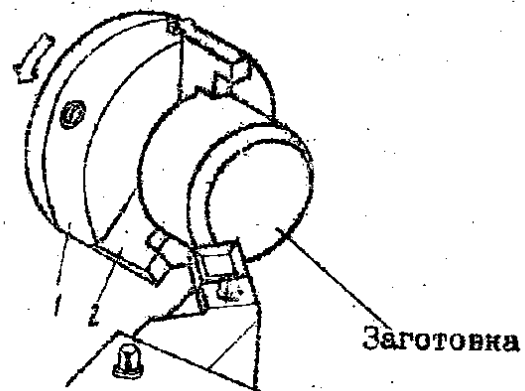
Закрепление заготовки в перевернутых кулачках патрона.
